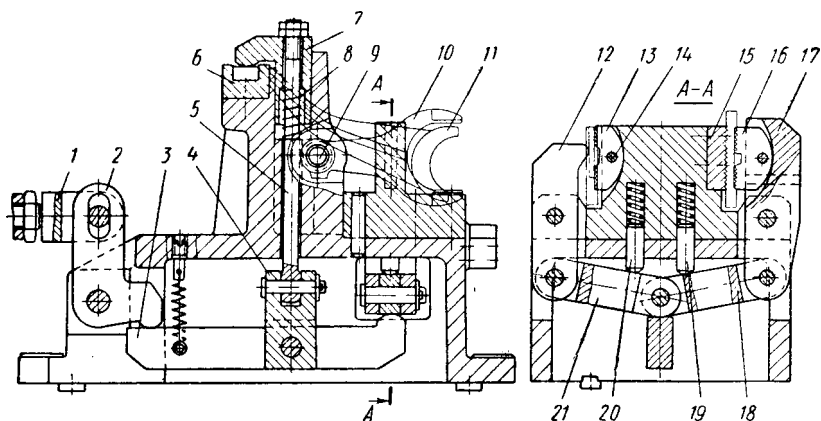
Двухместное приспособление для фрезерования боковых поверхностей
